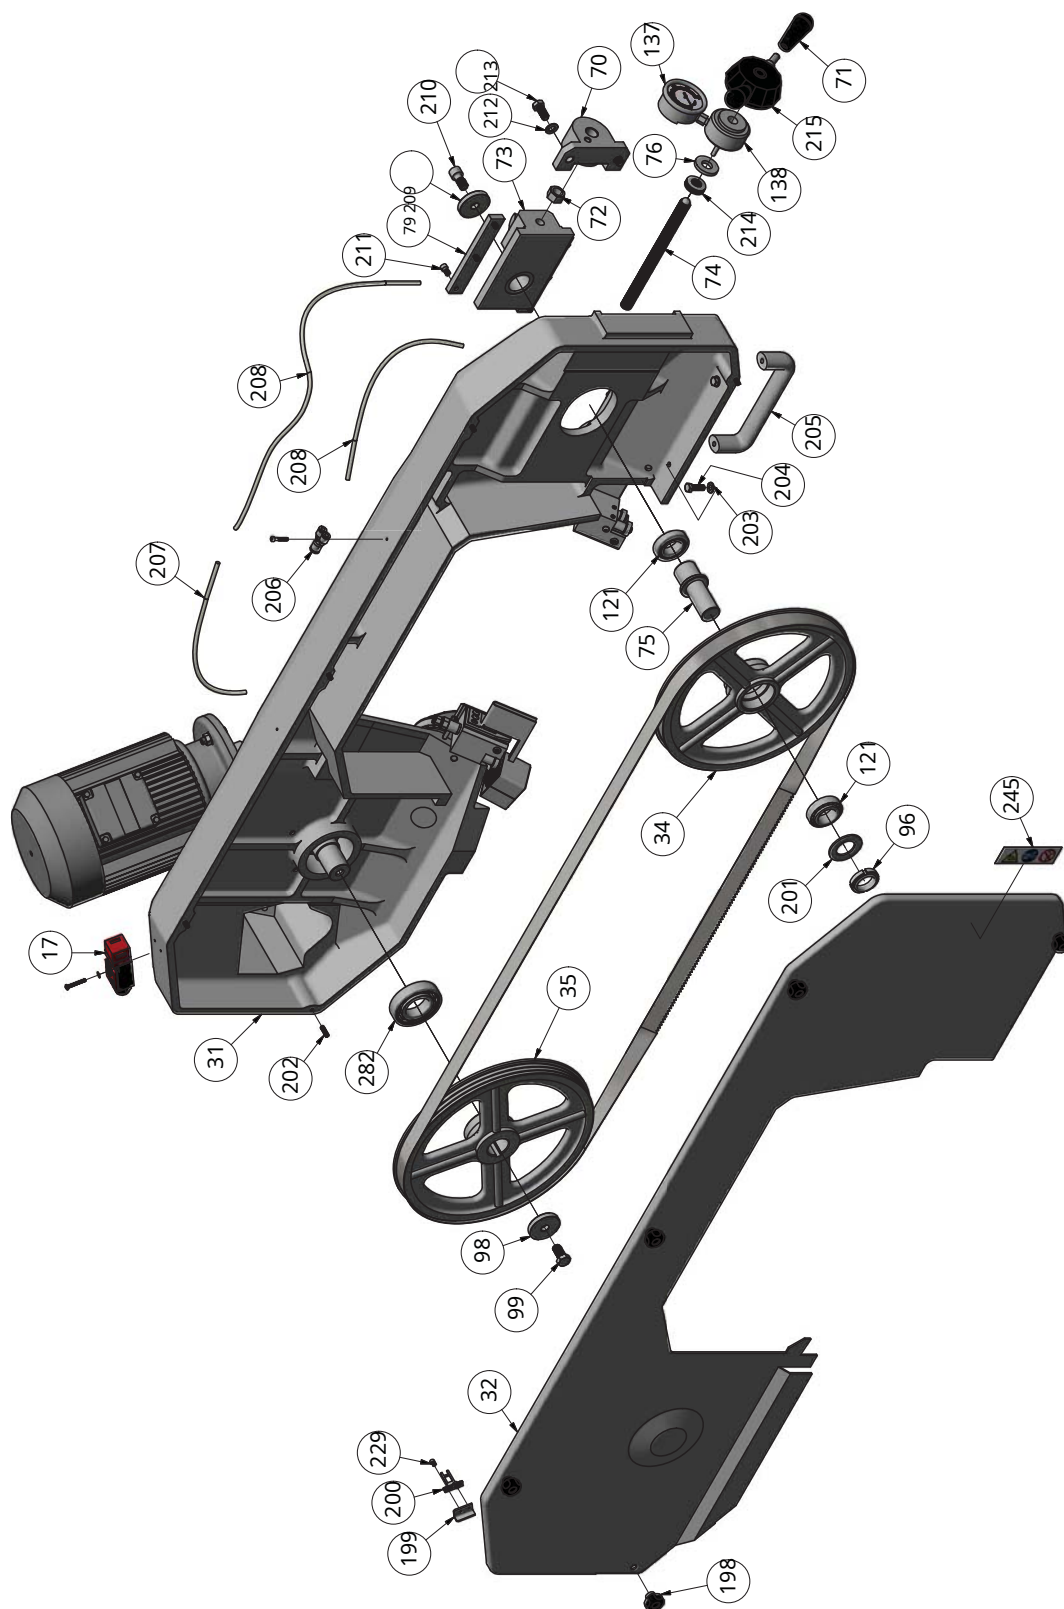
Explosionszeichnung - Dibujo de piezas de repuesto
